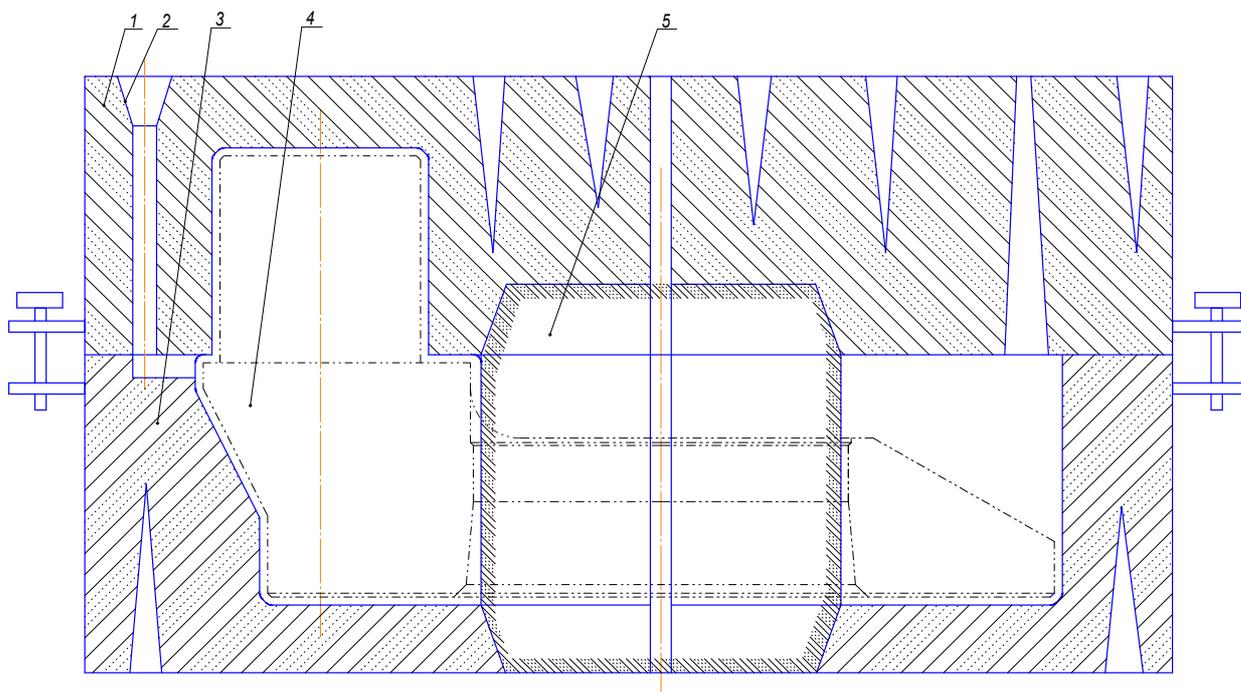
Песчаная разовая форма в сборе: 1-верхняя полуформа, 2-литниковая система (литниковая чаша и стояк), 3- нижняя полуформа, 4-отливка, 5- стержень.
